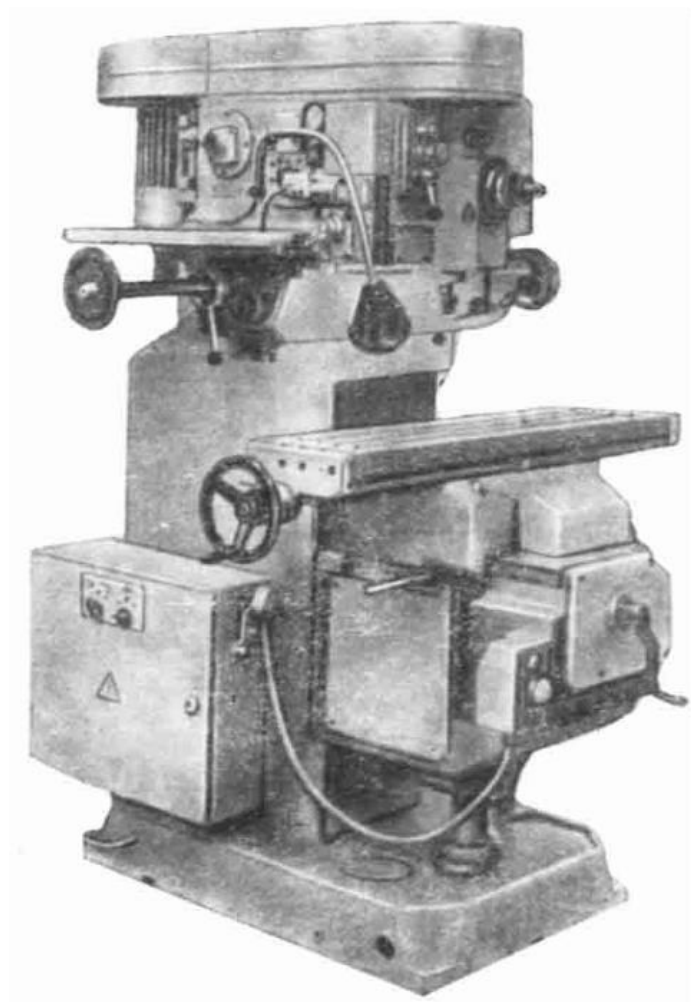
Шпоночно-фрезерный станок 692Д
